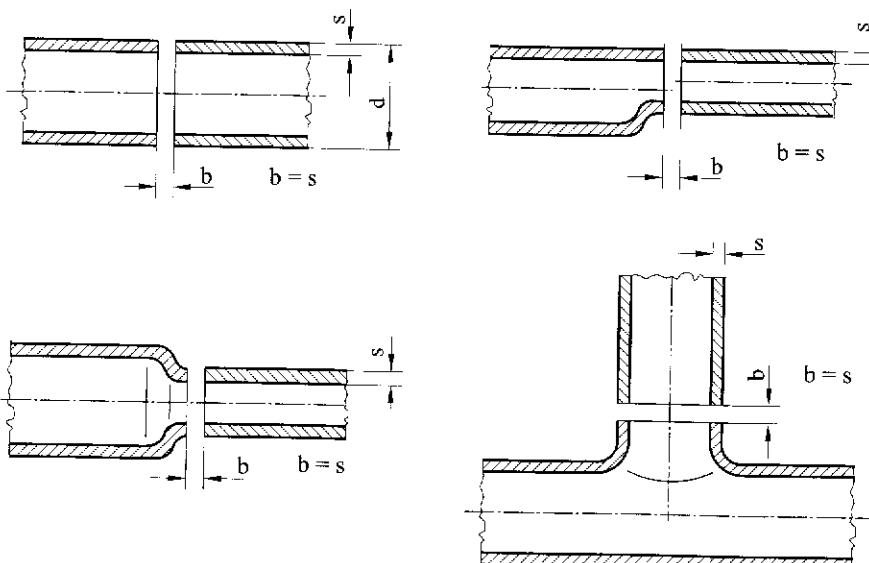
Соединения, свариваемые в медных трубопроводах
